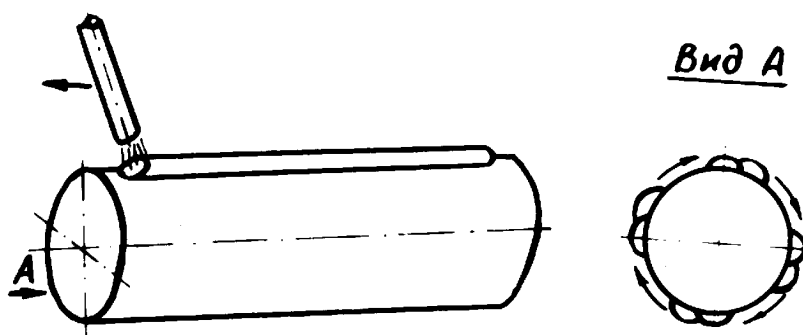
Наплавка тел вращения валиками вдоль образующей
